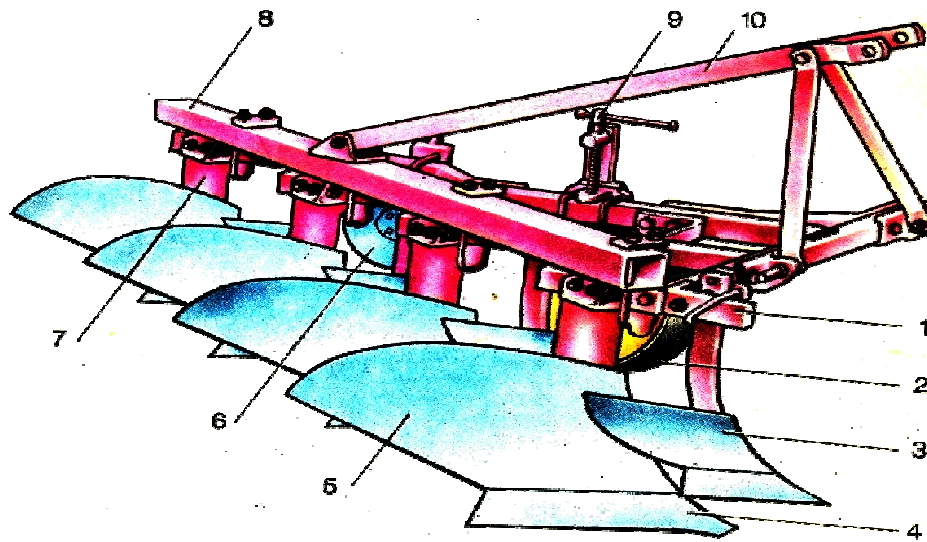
Плуг тракторний навісний чотирикорпусний ПН-4-35А: 1- рама; 2 – опорне колесо; 3 – передплужник; 4 – леміш; 5 – відвал; 6 – дисковий ніж; 7 – стійка; 8 – балка жорсткості; 9 – гвинт опорного колеса; 10 – підвіска.
